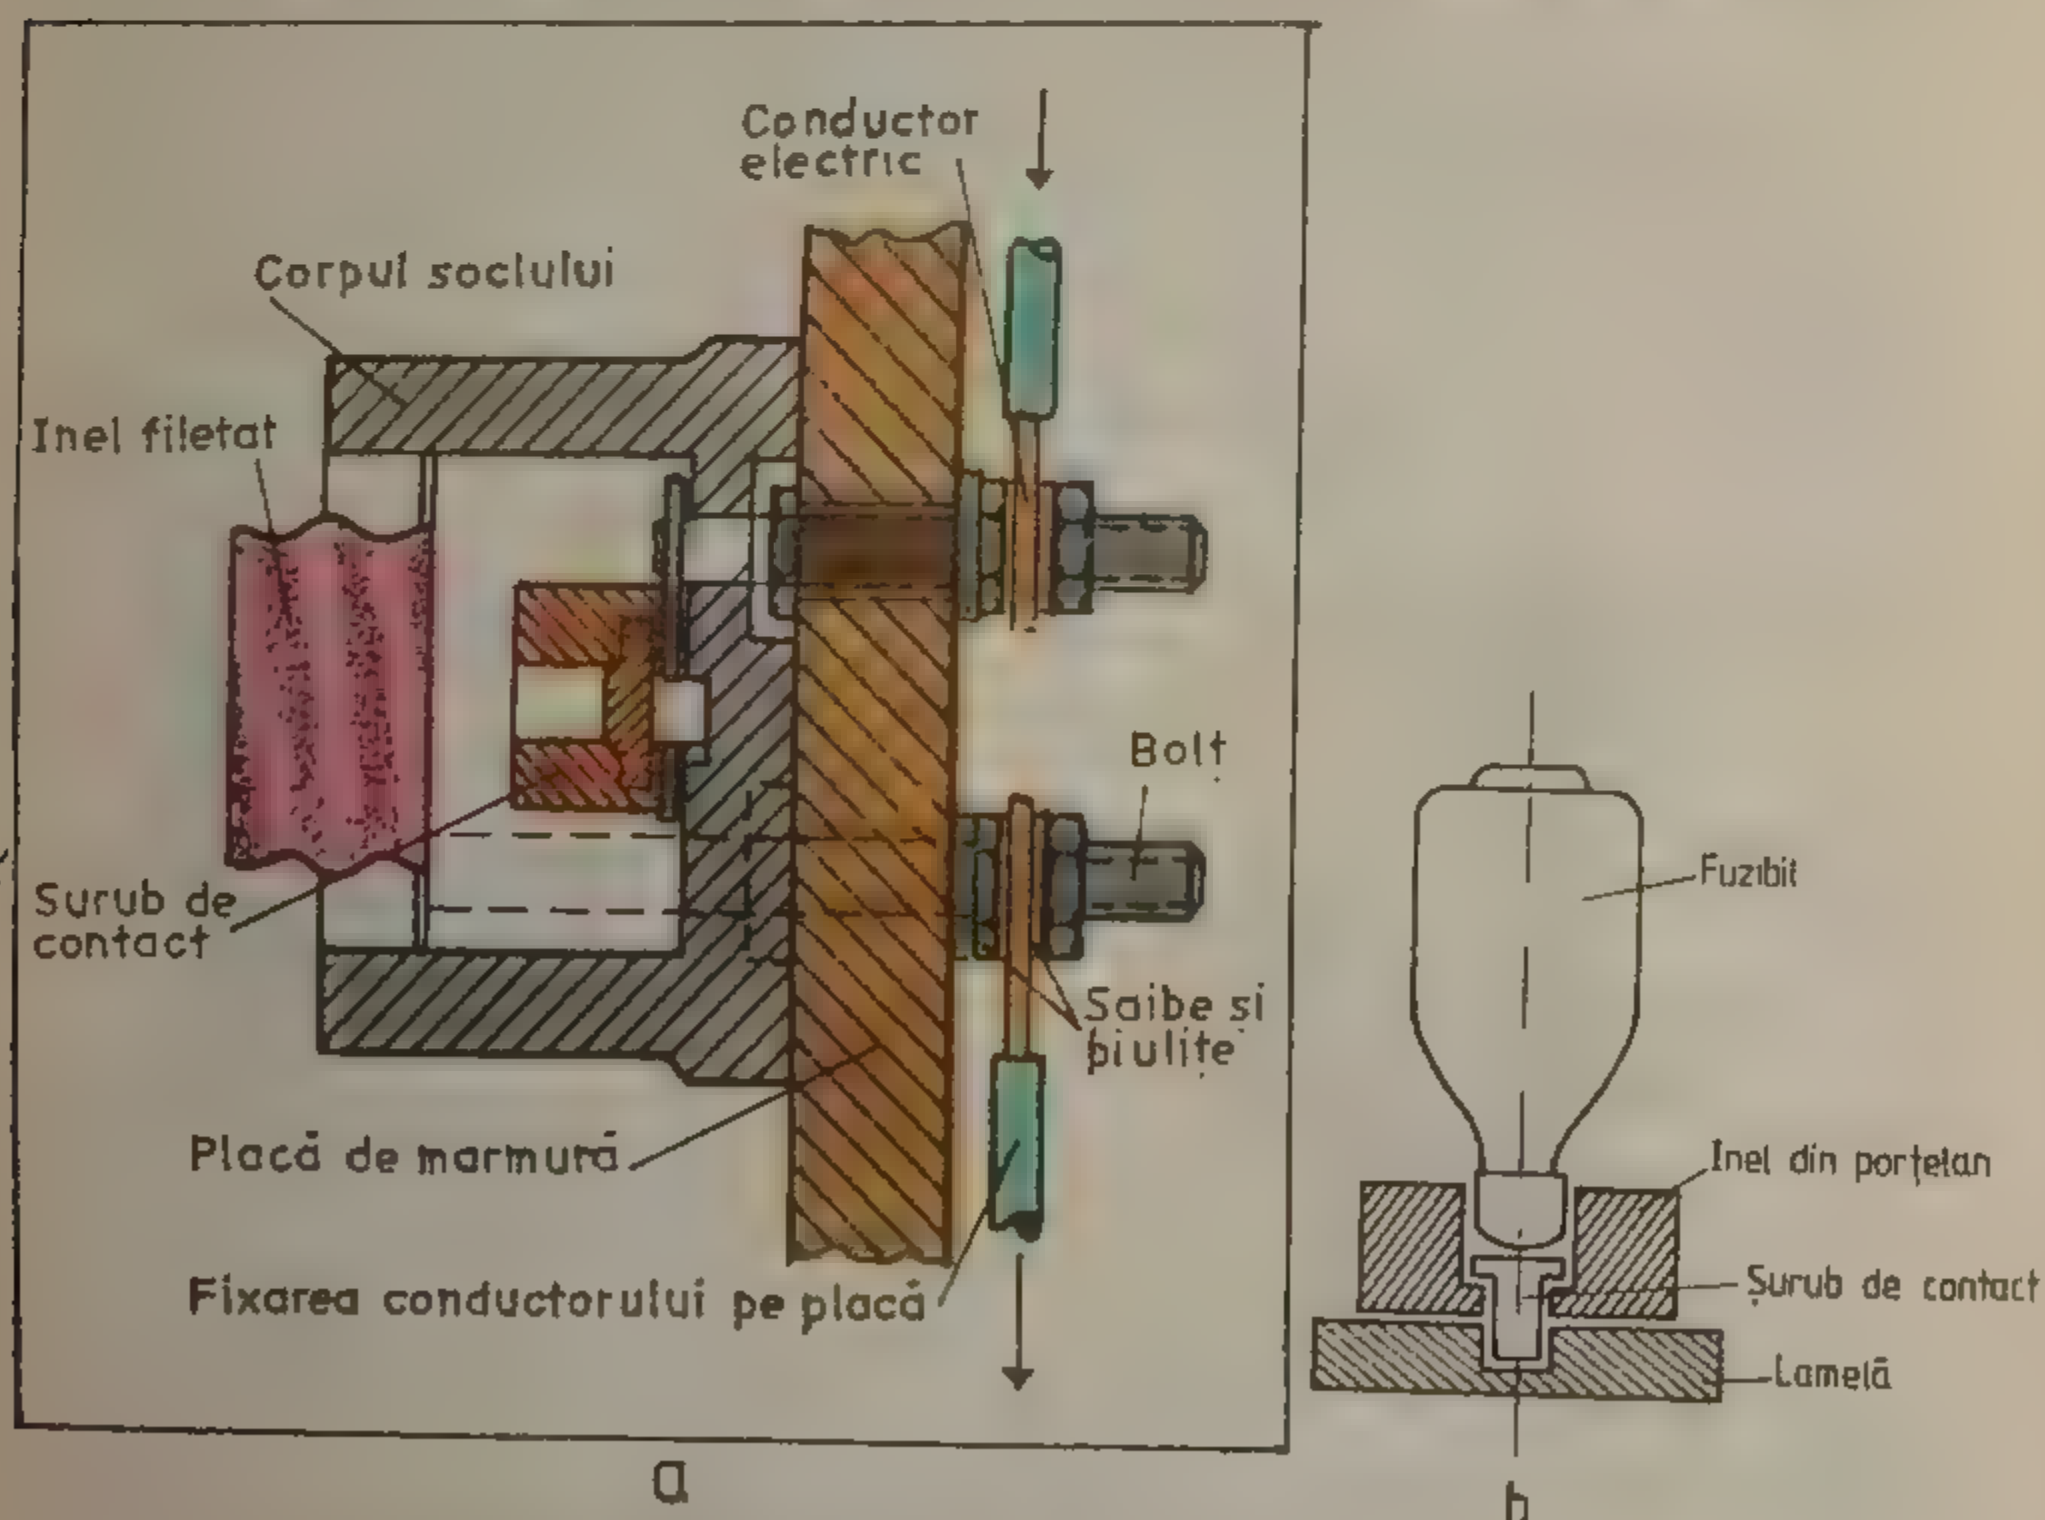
Elementele soclului unei siguranțe montată pe placa de marmură
